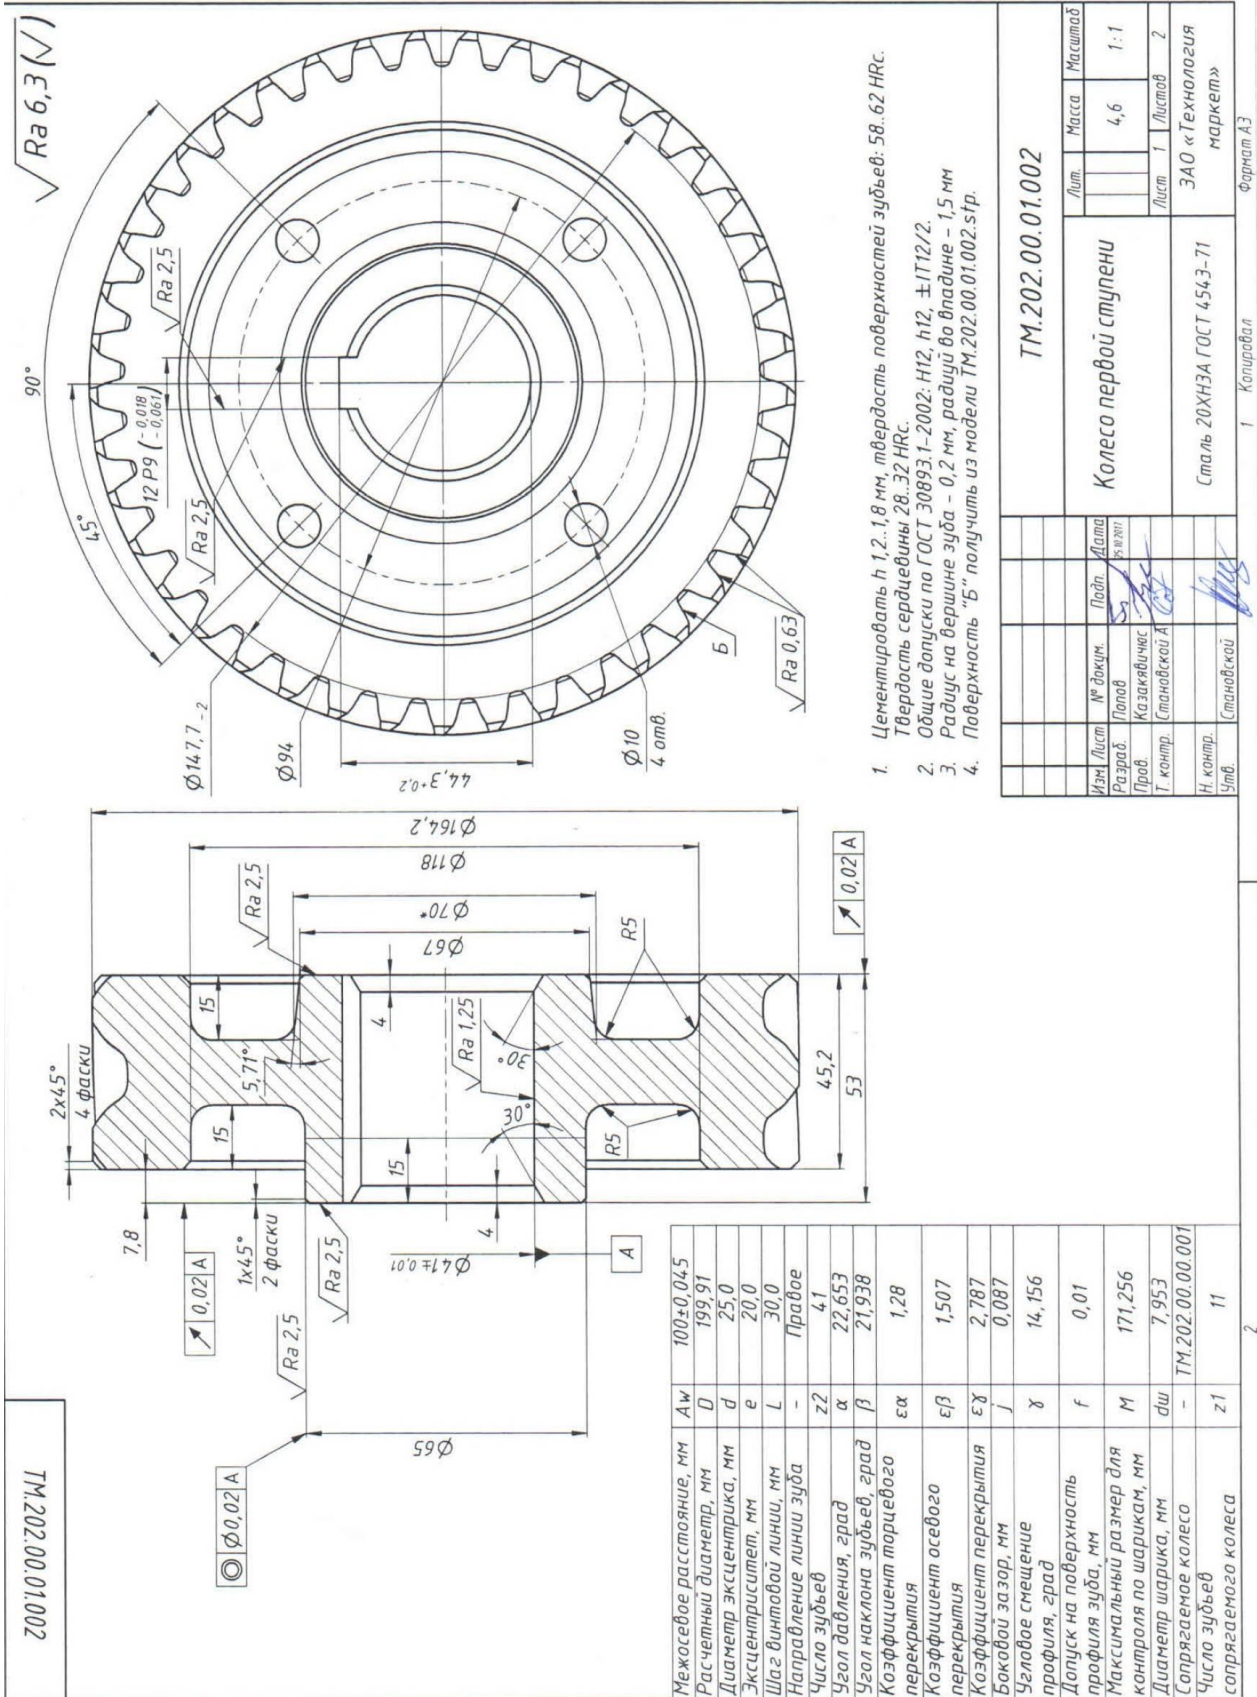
Чертеж колеса первой ступени редуктора с ЭЦ зубчатым зацеплением
